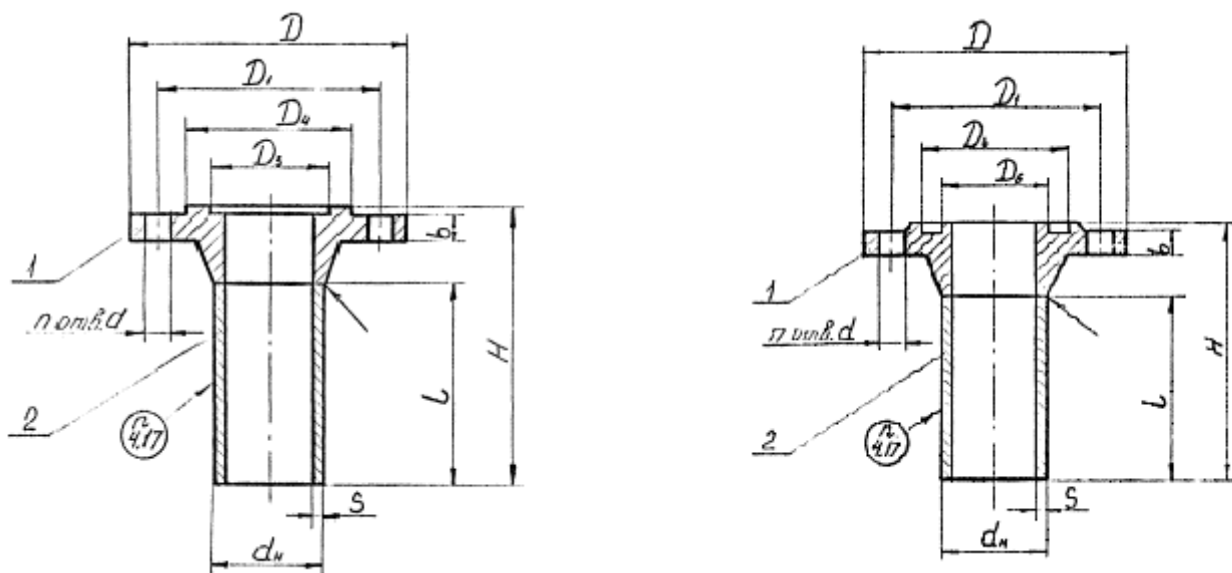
Штуцера с фланцами приваренными встык с уплотнительной поверхностью типа шип-паз на условное давление 4,0 МПа
